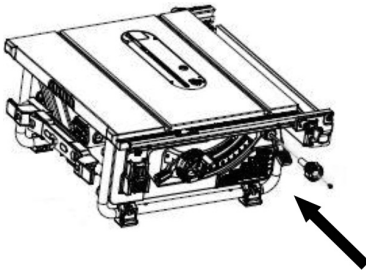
Instalando o manipulô de travamento do ajuste de corte
